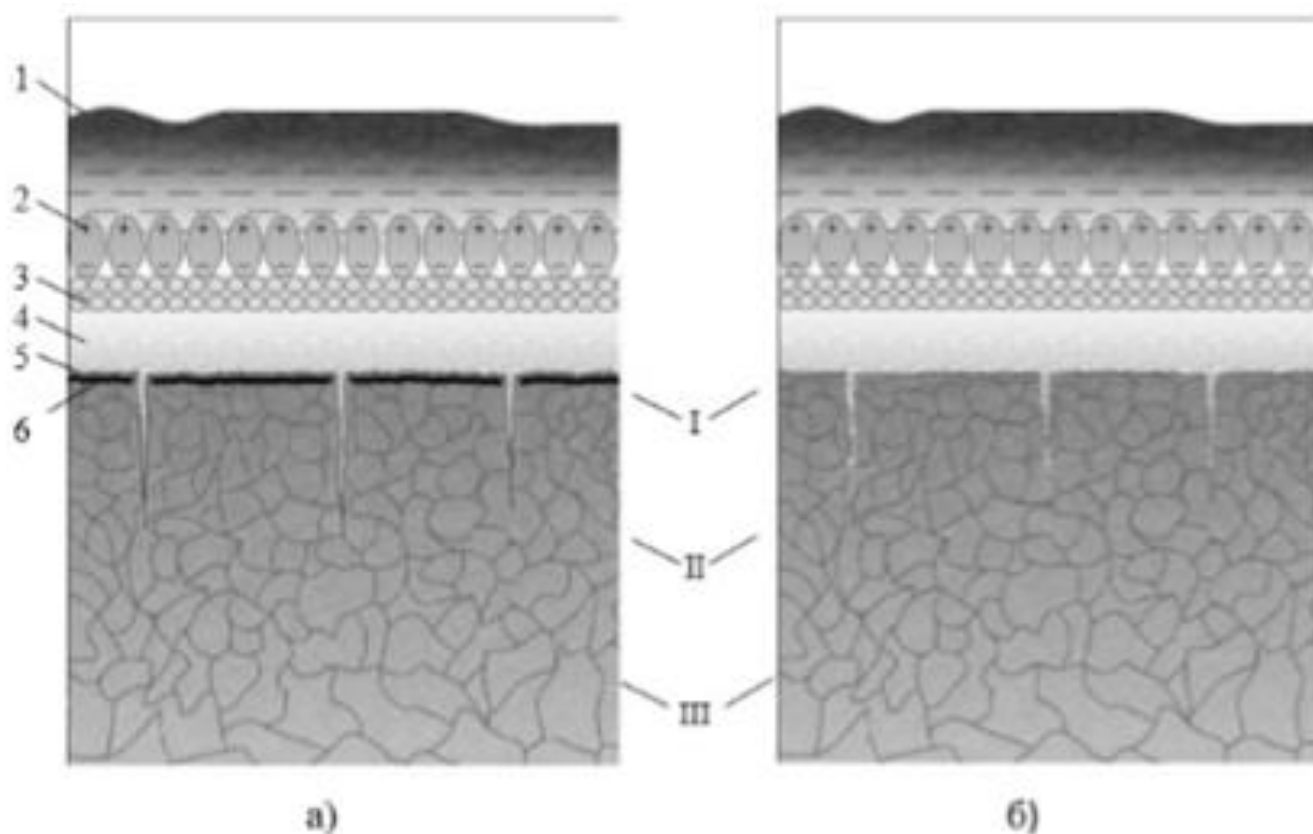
Поверхня металу в зоні різання після обробки:
